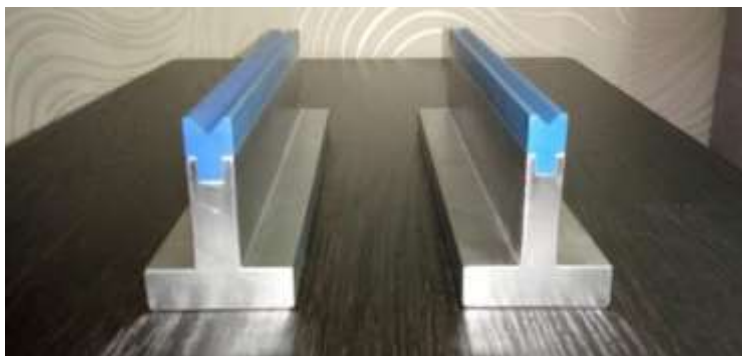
Комбинированный инструмент для гибки изделий сложного профиля.
